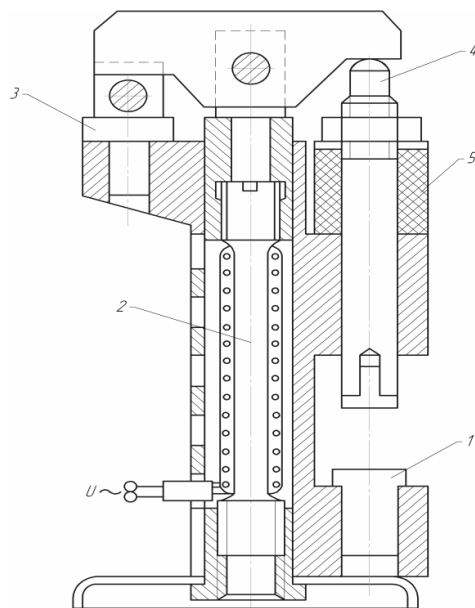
Прес для штампування з вузлами із матеріалу з ТМІ
